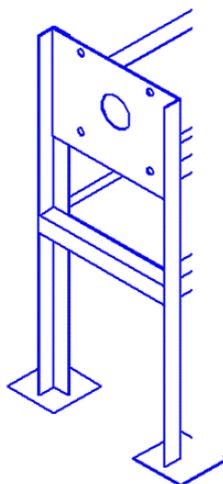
Пластина для крепления пневмоцилиндра к раме стенда.
